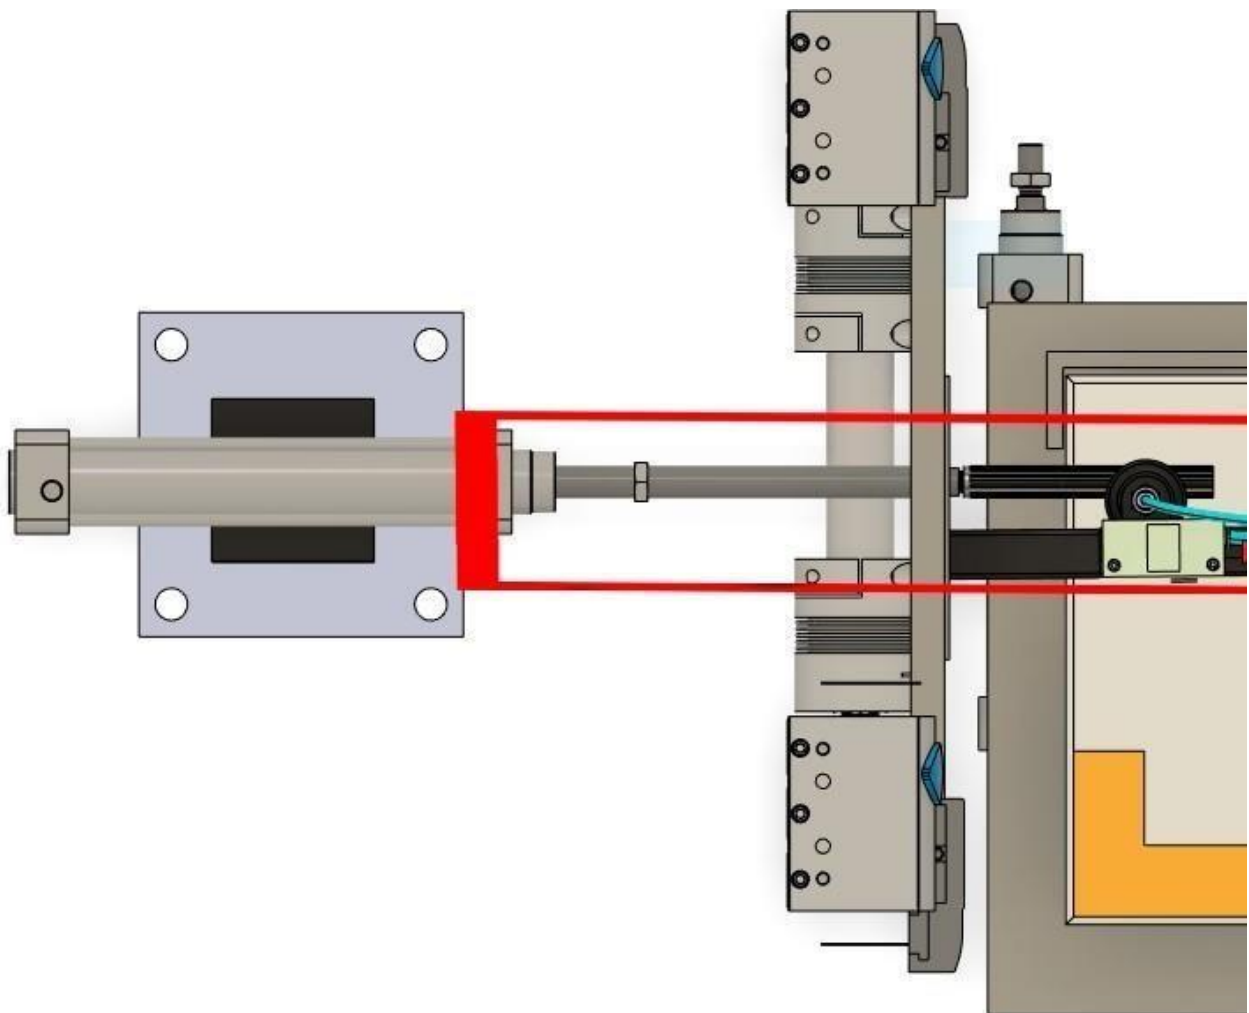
Пневмоциліндр FESTO для відкриття заготовки.
